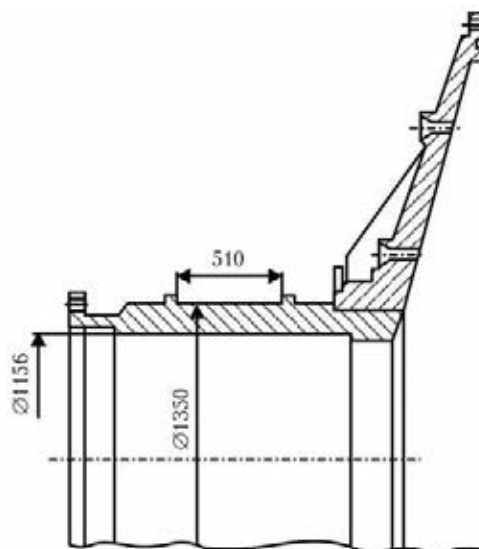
Наплавка цапфы мельницы сварочным полуавтоматом и эскиз цапфы
